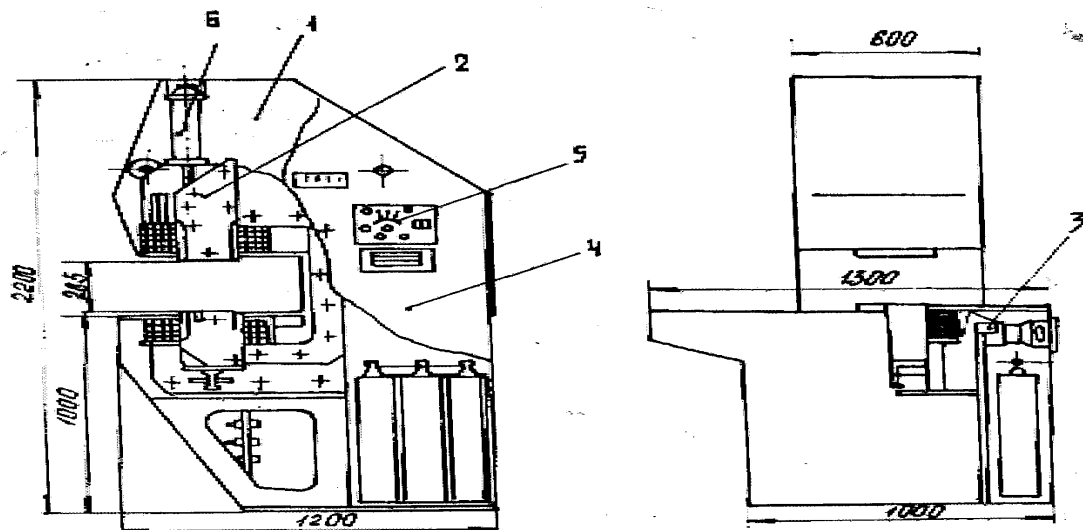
Индукционная установка ТПЧ для нагрева под сборку деталей локомотива: 1 - корпус, 2 - индуктор, 3 - механизм ввода термодатчика, 4 - шкаф с электроаппаратурой, 5 - панель управления, 6 - пневмопривод.
